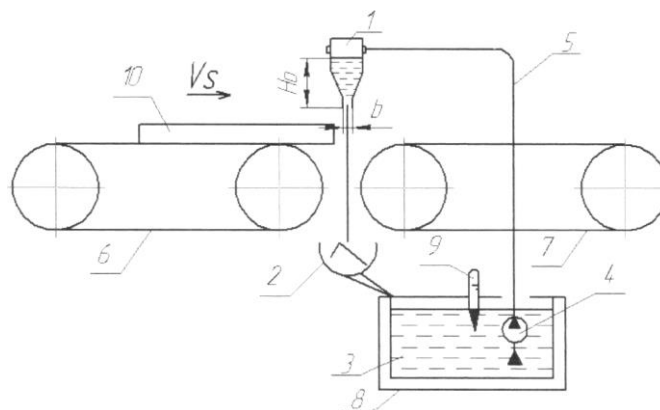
Принципова схема лаконаливної машини для пластей:
